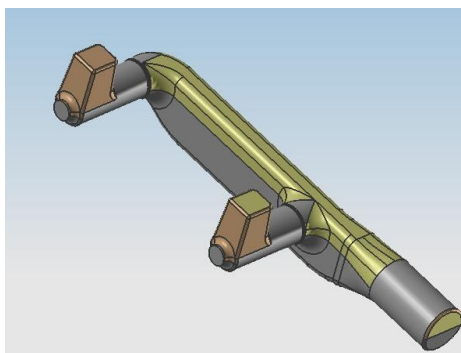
Стержень для отливки «Коллектор» 245-1003033Д
